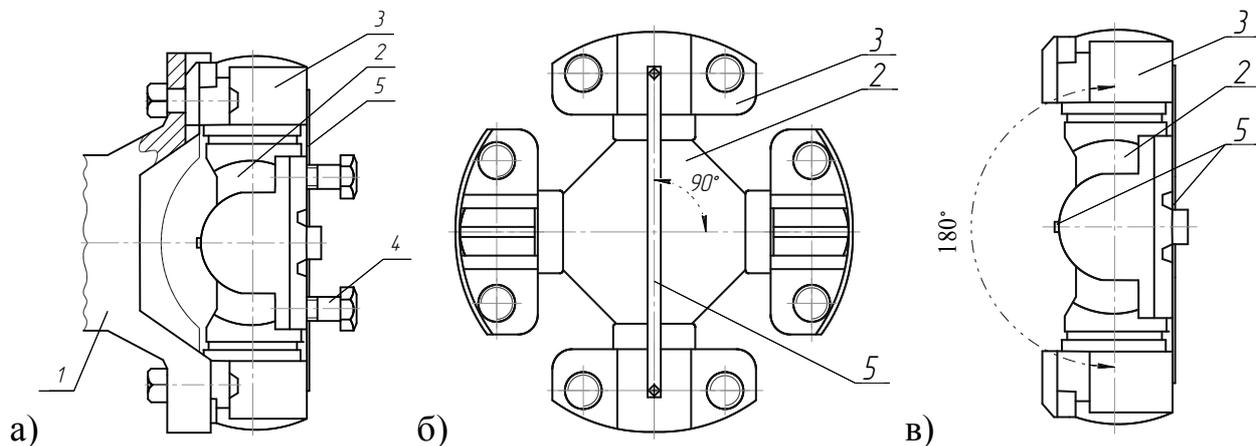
Способ замены рабочих поверхностей подшипниковых узлов карданных шарниров: а) схема шарнира; б) схема поворота крестовины на 90° ; в) схема поворота крестовины на 180° ; 1 – фланцы; 2 – крестовина; 3 – корпуса игольчатых подшипников; 4 – винты; 5 – стальная лента
